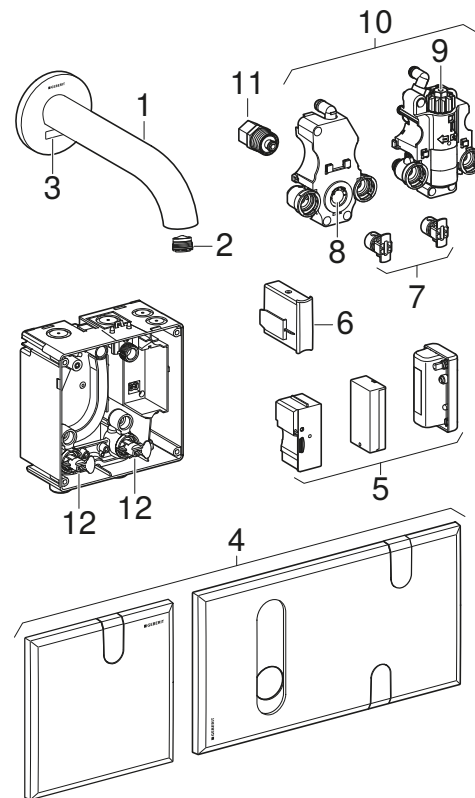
Baterii de lavoar Geberit Piave și Brenta, montaj pe perete
